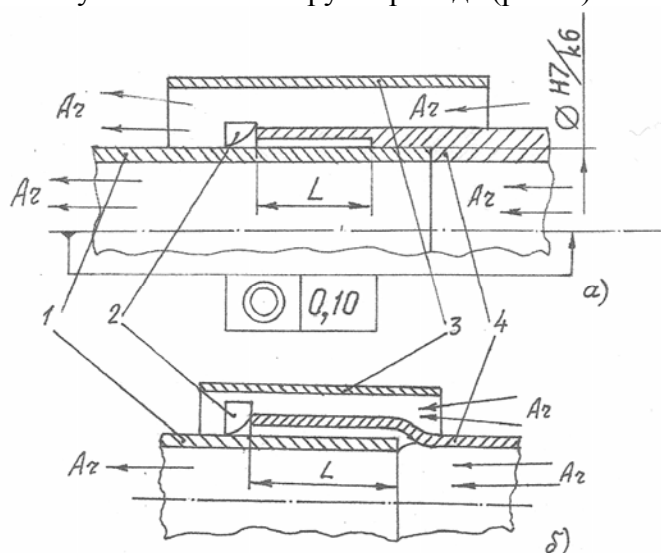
Схемы пайки труб: а) с корпусными деталями; б) телескопических соединений.
